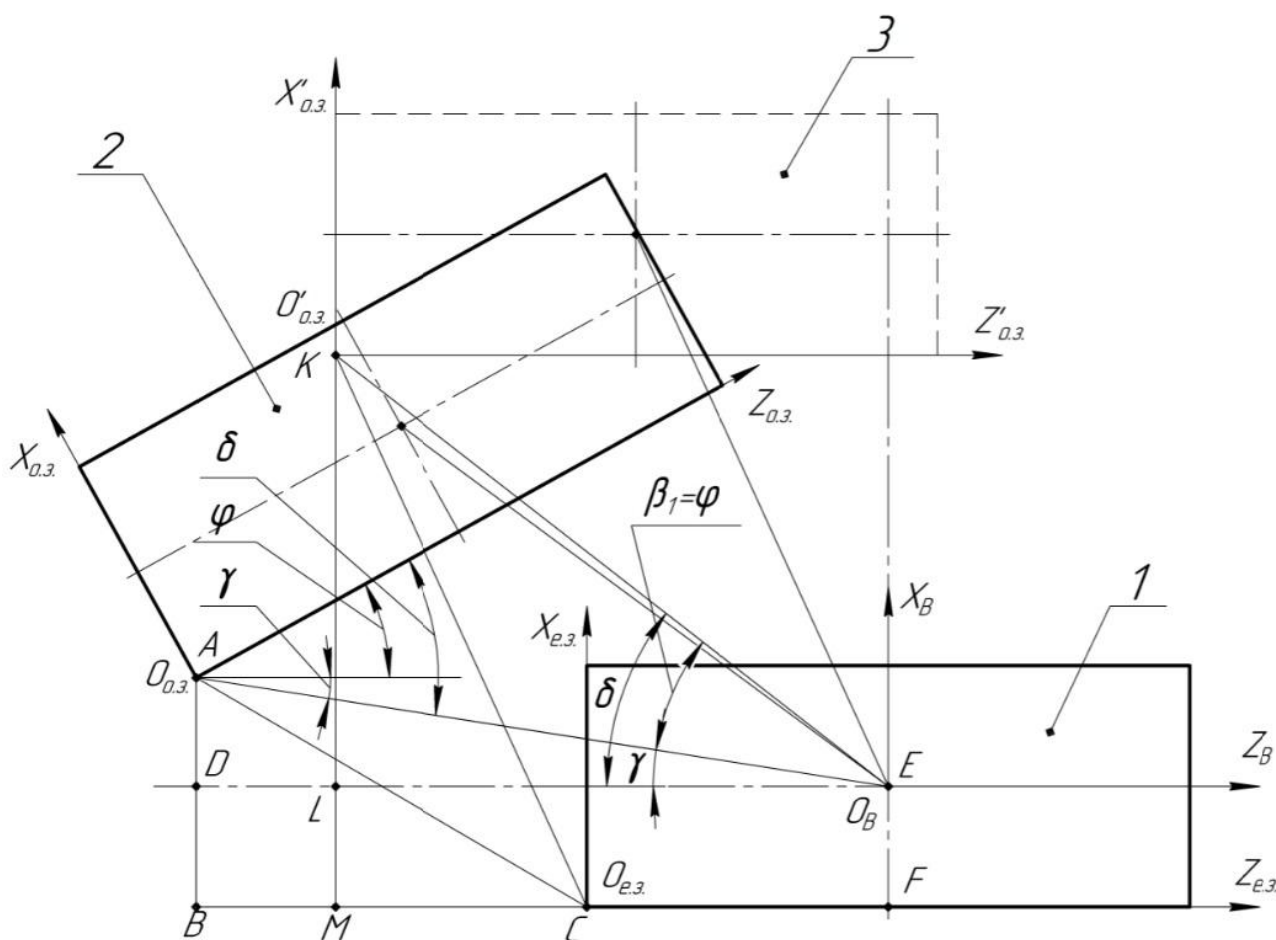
Розрахункова схема розташування еталонної заготовки 1, оброблюваної заготовки в вихідній позиції 2 та оброблюваної заготовки в робочій позиції 3
